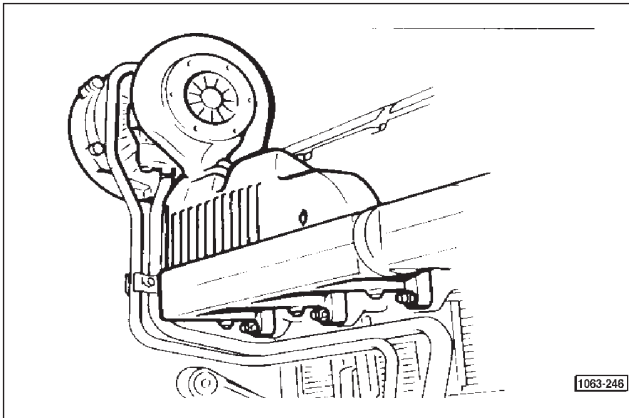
Dans les moteurs suralimentés: installer l'ensemble du turbocompresseur en observant les instructions reportées à la page 91.
